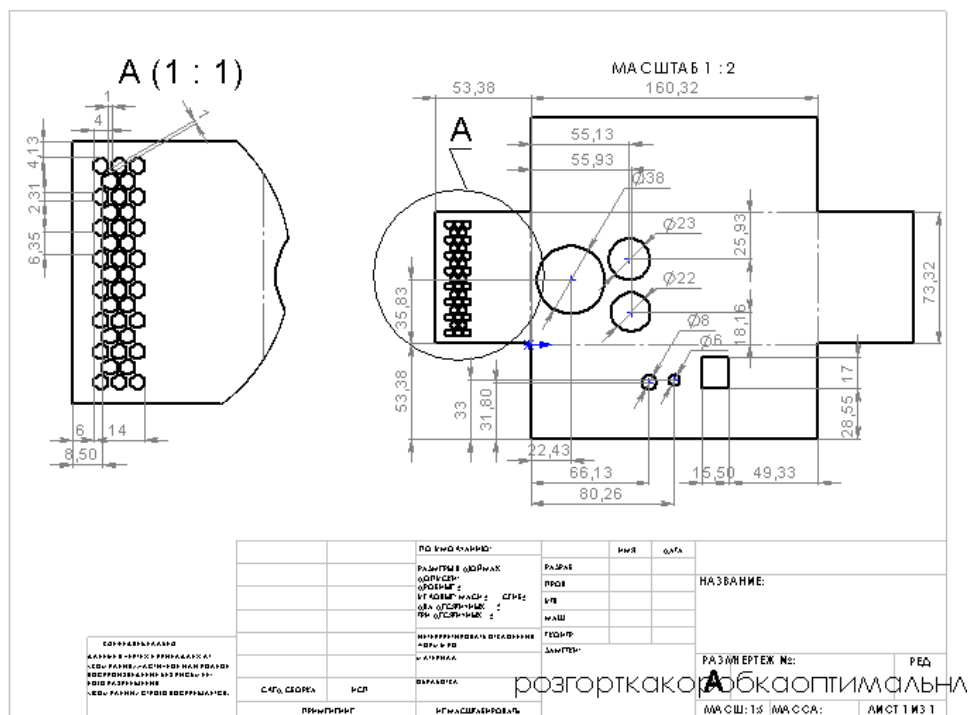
Оптимальна комплектація з металу нижня частина корпусу блоку керування.
